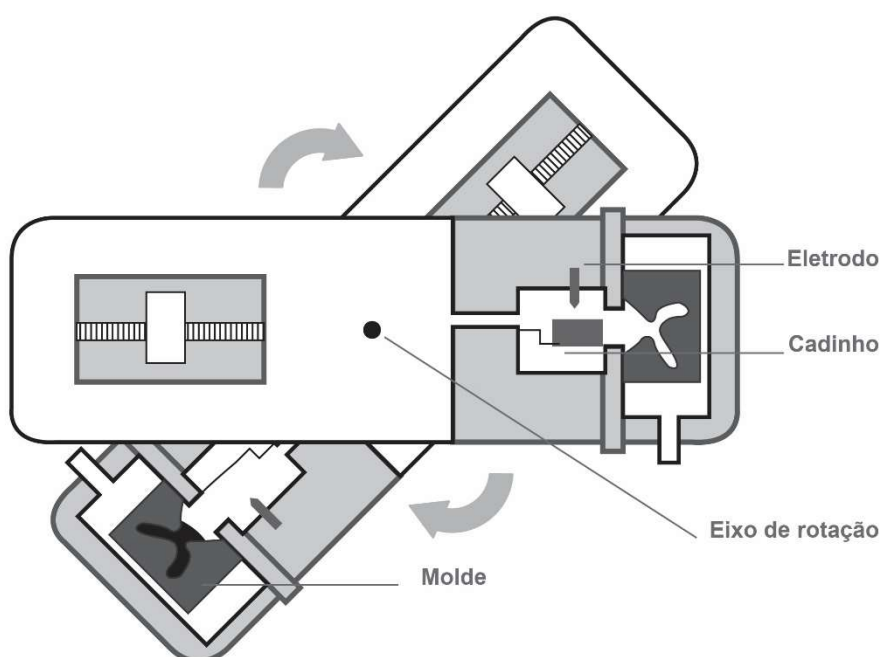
Máquina Vulcan-T equipada com câmara única sob pressão de gás (vista Superior). Adaptada (Okabe *et al.*, 1998).
